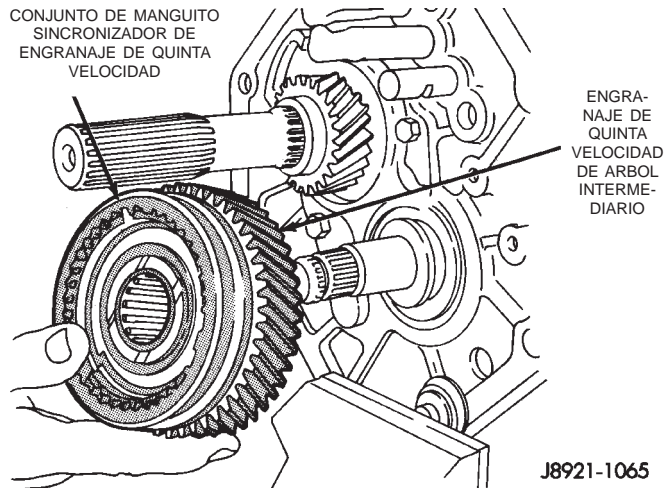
Desmontaje del conjunto de sincronizador y engranaje de quinta velocidad
